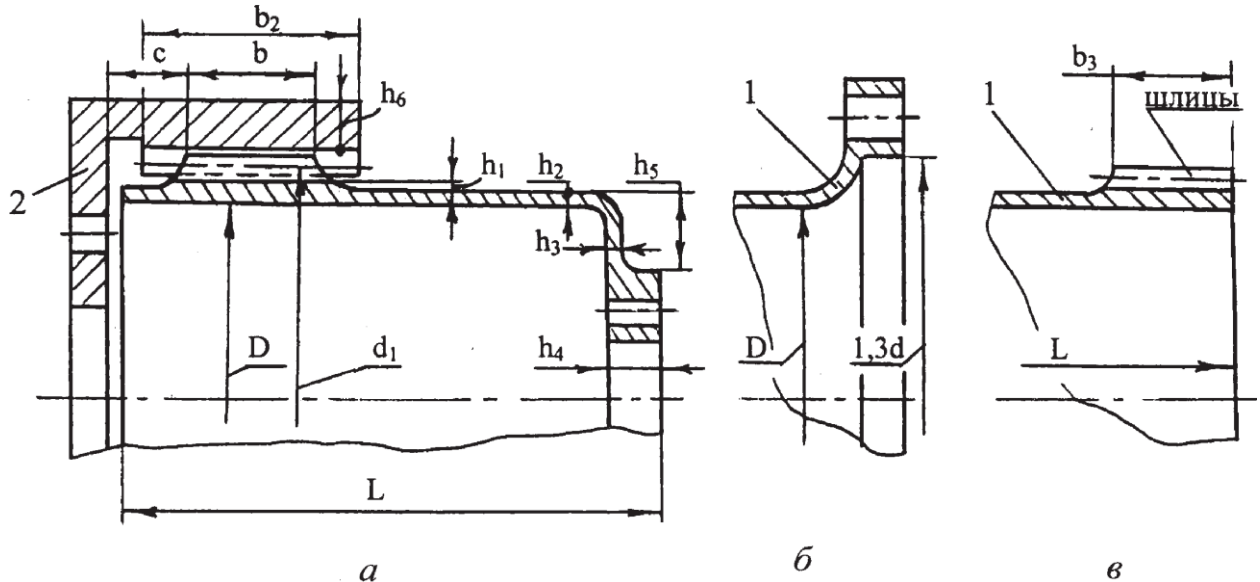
Геометрические параметры волновой передачи: *a* — типовая конструкция передачи; *б* — вариант исполнения фланца гибкого колеса; *в* — гибкое колесо со шлицами
